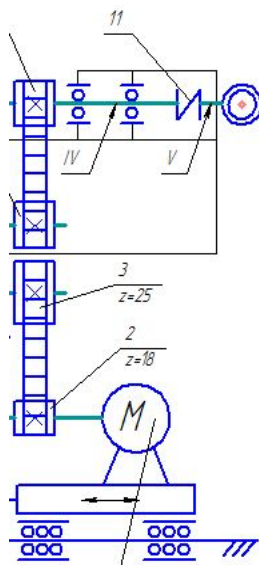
Фрагмент кінематичної схеми приводу оброблювального центру
